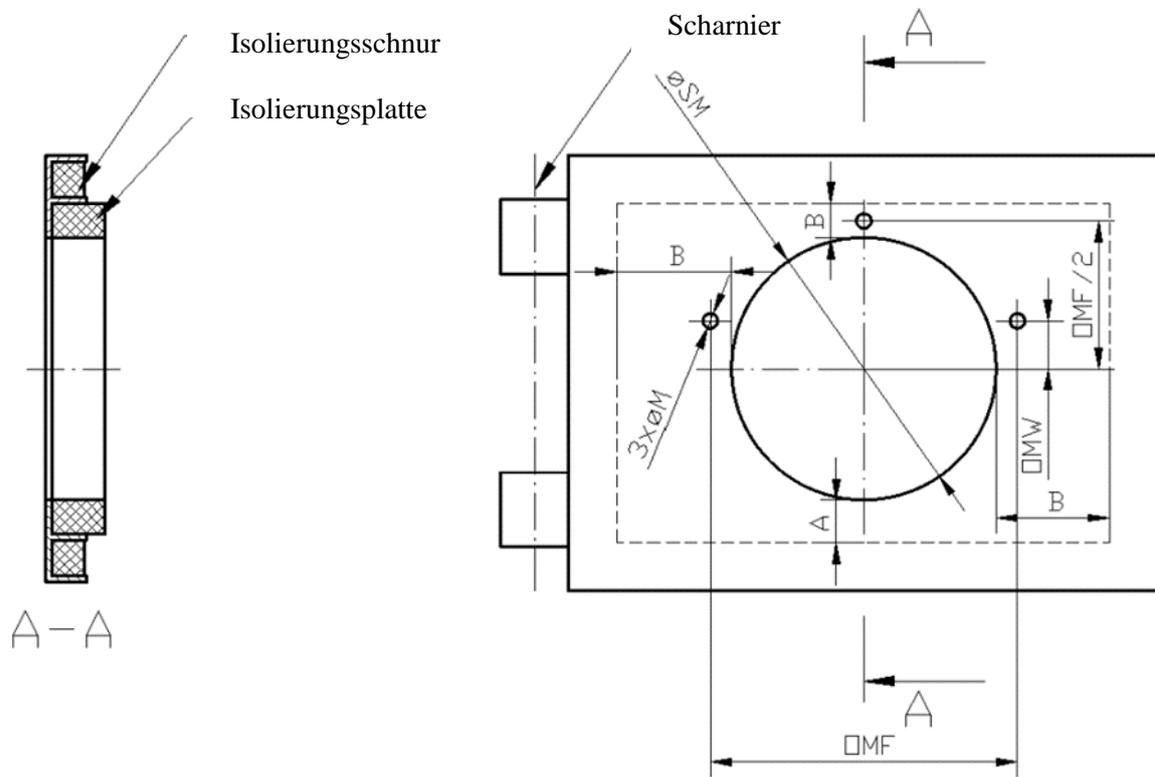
Schema der Herstellung von Montagebohrungen für Brenner mit einem Wärmedämmmantel und einer Montageplatte für Brenner 10-50 kW
